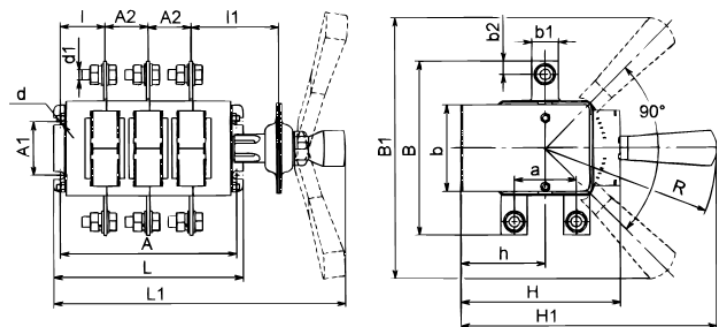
Б Выключатель-разъединитель на два направления трехполюсный с боковой смещенной рукояткой
